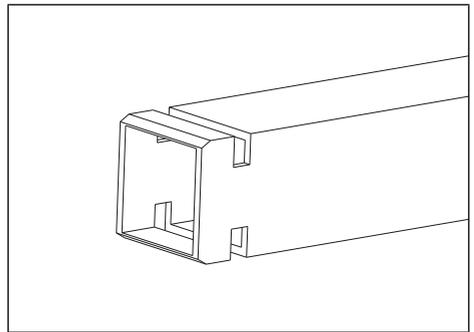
Évidements dans la poutre transversale Multi Wall
